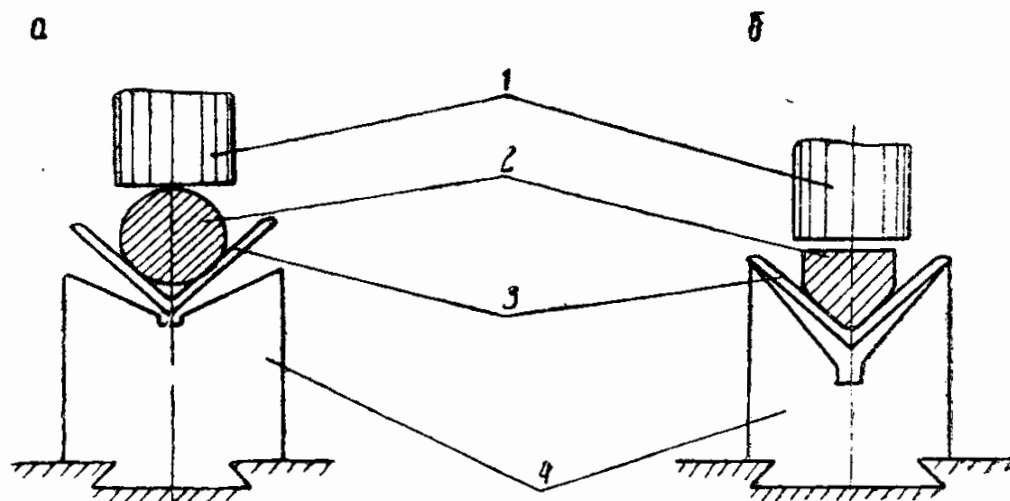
Приспособление для размалковки (а) и смалковки (б) уголков: 1 — боек; 2 — прокладка; 3 — обрабатываемый уголок; 4 — нижний штамп.
